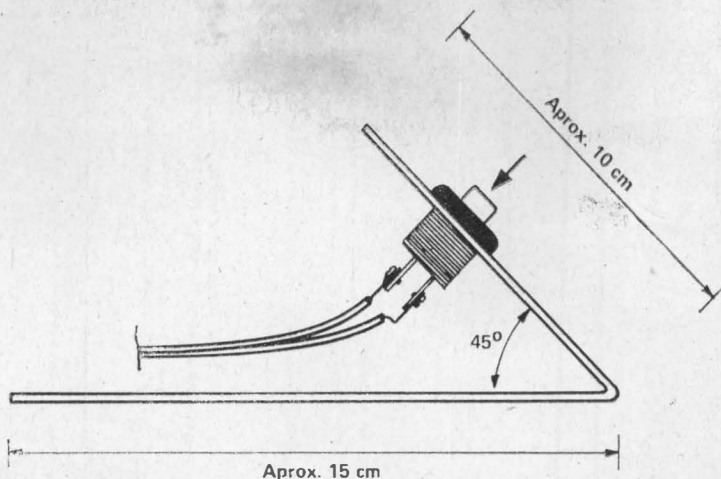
Aspecto do pedal onde é instalado o interruptor do controle remoto.
